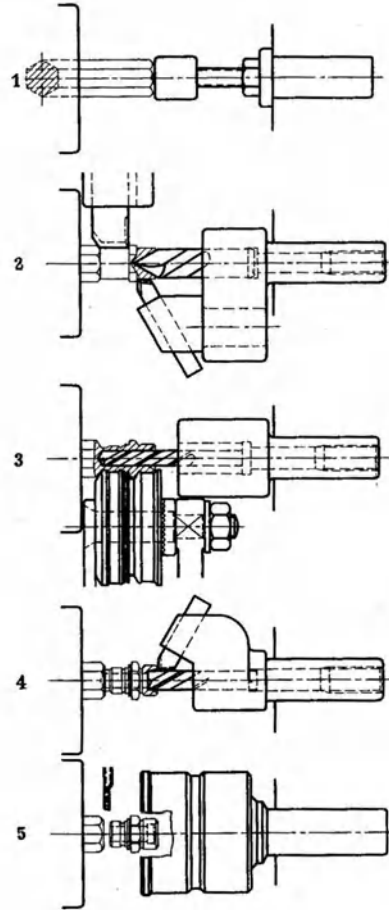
Bearbeitung einer Verschraubung aus Duralumin.
